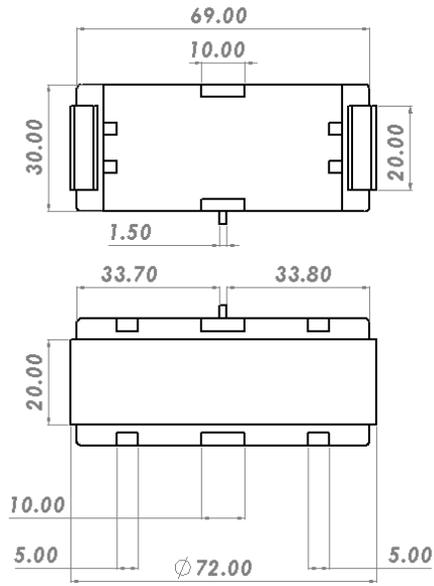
Planos vista posterior e inferior del dispositivo vibrador final.
